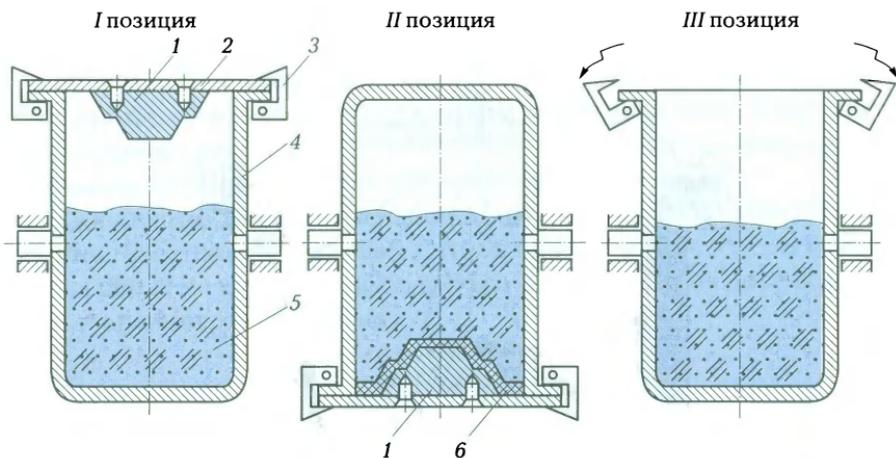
Бункерный способ изготовления оболочковых полуформ:
